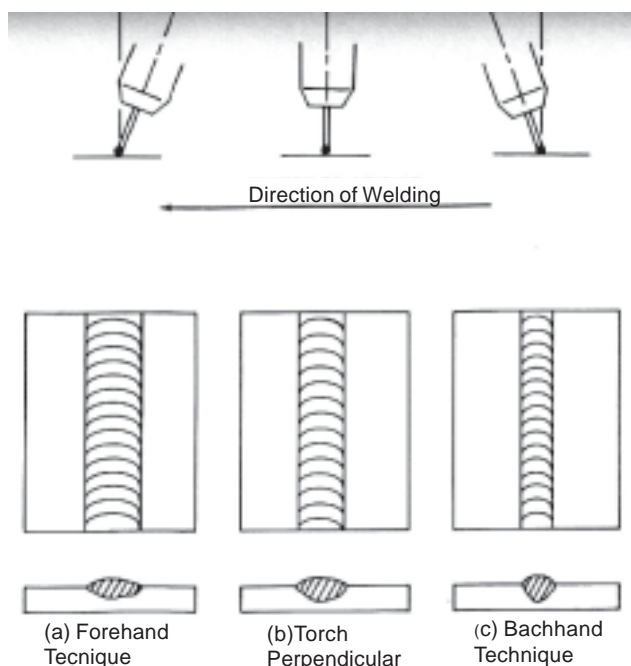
Efeito da posição do eletrodo e da técnica de soldagem.
